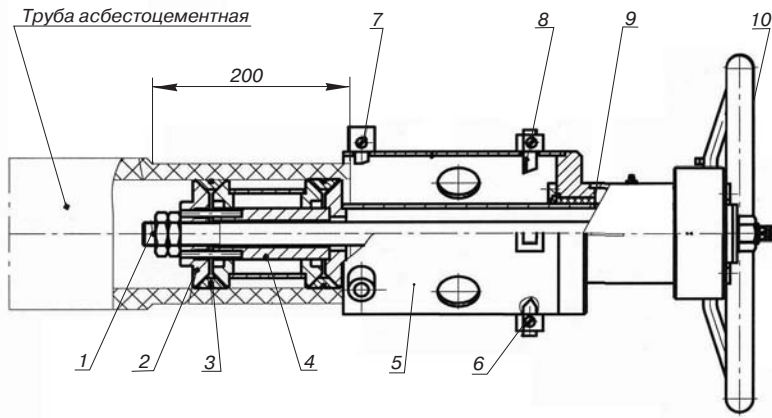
Ручное приспособление для обточки асбестоцементных труб: 1 – винт; 2 – упор; 3 – су-харь с пружинным кольцом; 4 – распорка; 5 – корпус; 6 – резец для выполнения фаски (2 шт.); 7 – резец для обточки наружного диаметра (3 шт.); 8 – резец для обточки торца (2 шт.); 9 – направляющая; 10 – маховик
